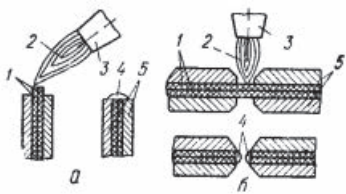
Схема сварки пленок оплавлением кромок: с подготовкой свариваемых кромок (а) и без подготовки свариваемых кромок (б): 1 – свариваемые пленки, 2 – струя газа, 3 – наконечник нагревателя, 4 – сварной шов, 5 – зажимные губки
